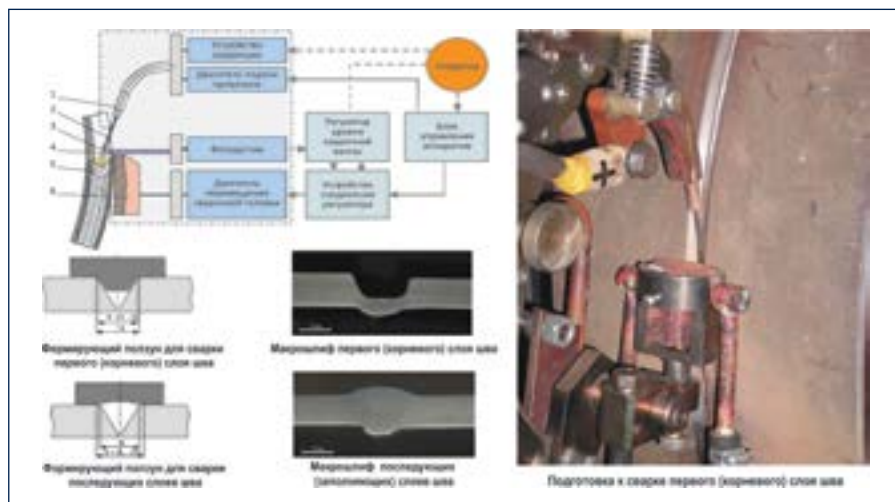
Комплекс автоматической сварки порошковой проволокой в среде углекислого газа с принудительным формированием металла шва
